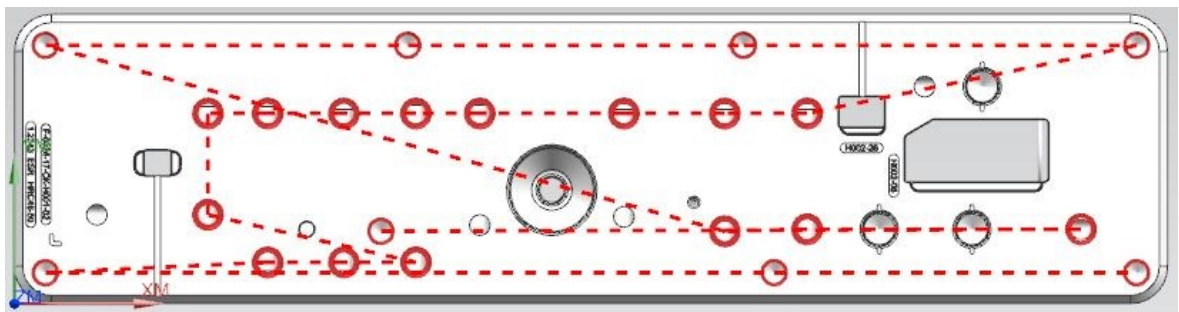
Dráhy vrtání zahloubení u děr o průměru 10mm
